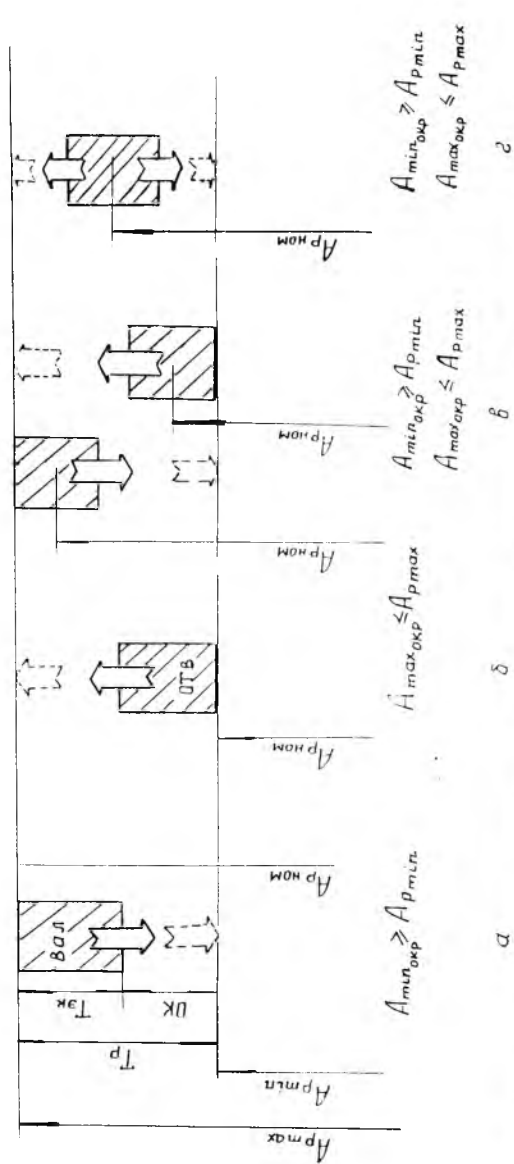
Схема округления операционных размеров, определяемых из размерных цепей, замыкающими звеньями которых являются конструктивные размеры:  $a$  — для размеров типа «вал»;  $b$  — для размеров типа «отверстие»;  $\delta$  — для размеров заготовки и других;  $a$ ,  $b$ ,  $\delta$  — расчет по методу максимальных размеров,  $\delta$  — расчет по вероятностному методу
